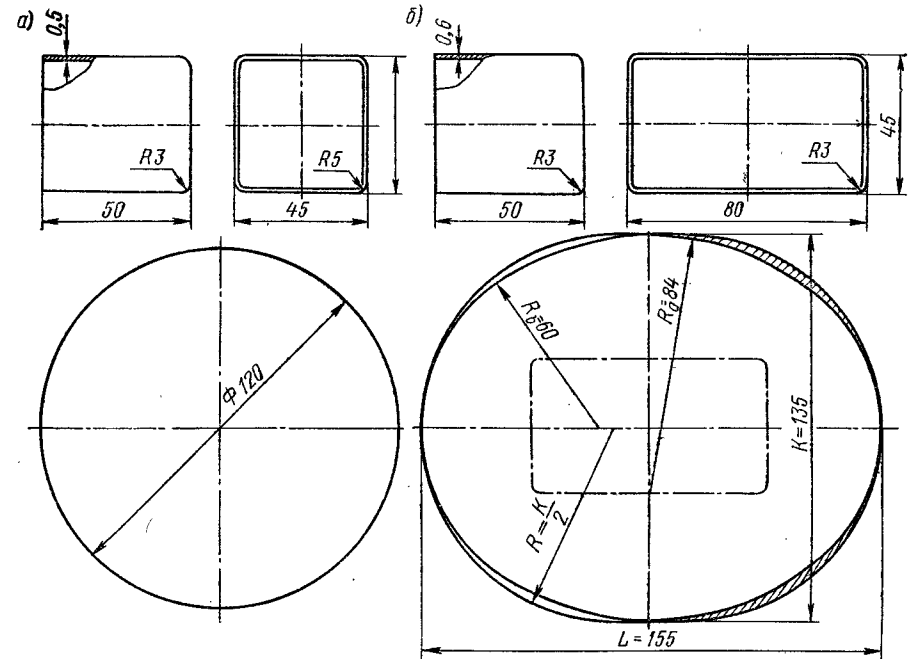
К расчету размеров заготовки для коробчатых деталей
